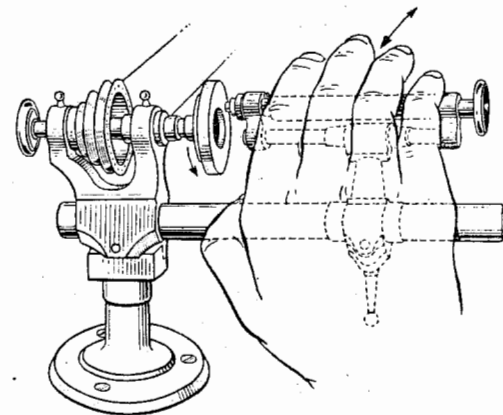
Обточка цилиндрических деталей с помощью суппорта.
